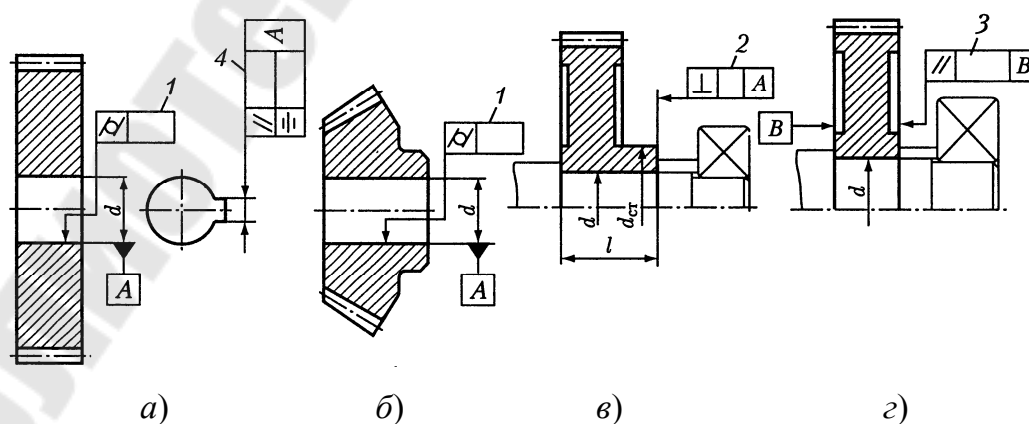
Указание на чертеже зубчатого колеса допусков формы и расположения
